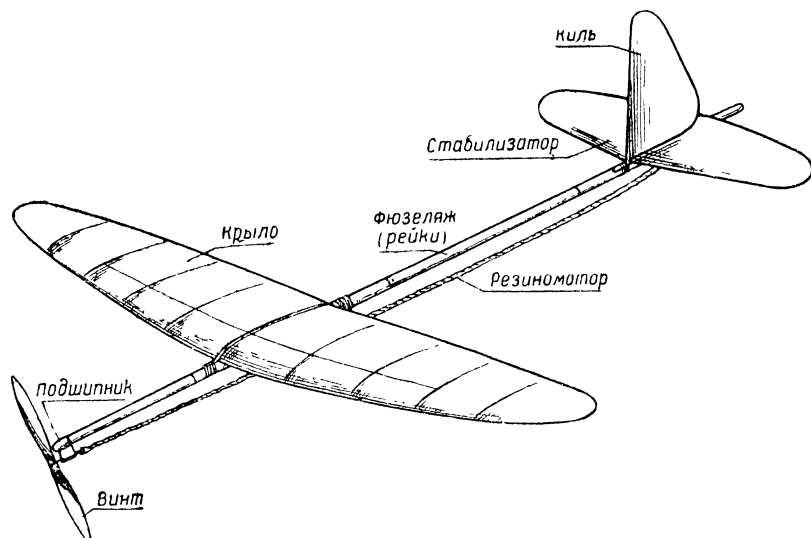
Общий вид схематической летающей модели самолета тракторного типа конструкции Лесика Нестеренко
